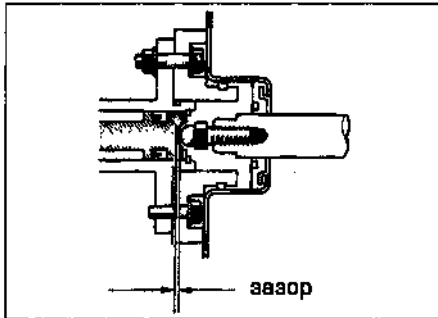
, а. Между поршнем главного цилиндра и толкателем вакуумного усилителя должен быть небольшой зазор
